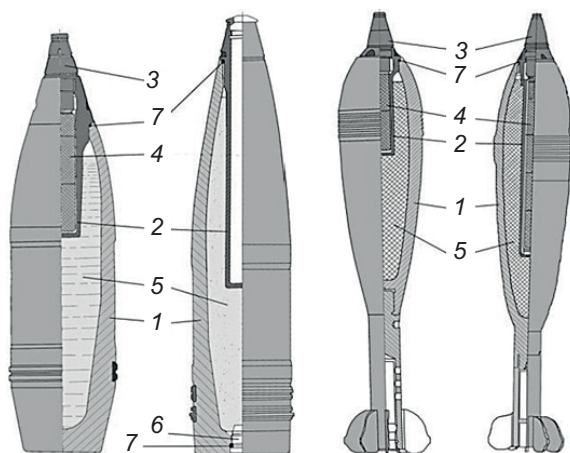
Схема устройства различных типов дымовых БП: 1 – корпус; 2 – запальный стакан; 3 – взрыватель; 4 – разрывной заряд; 5 – дымообразующее вещество; 6 – пробка; 7 – свинцовая прокладка
